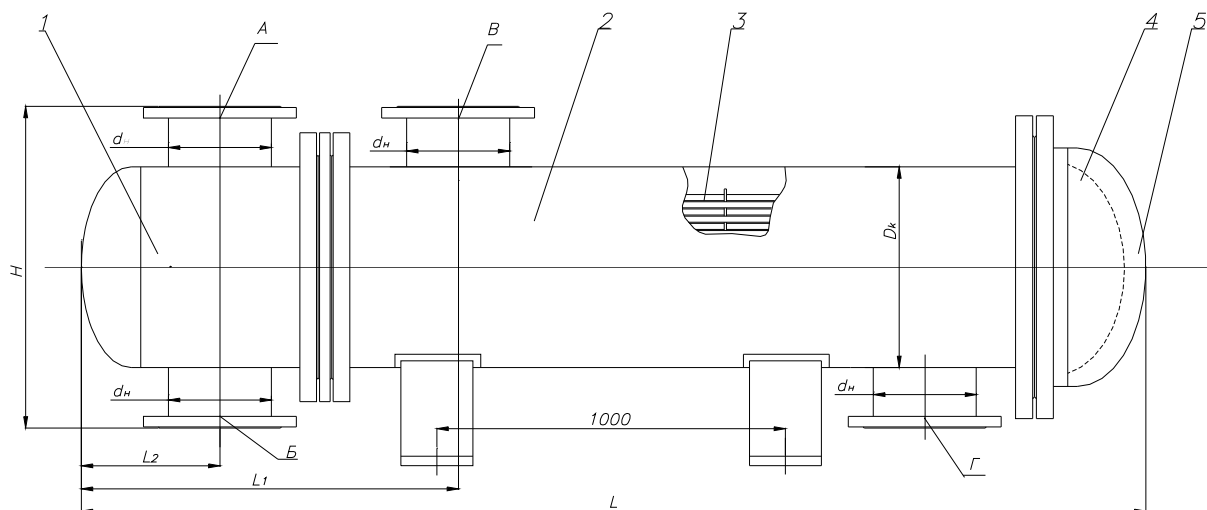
Схема подогревателя ПВМР: 1 – камера распределительная; 2 – корпус; 3 - трубная система; 4 – малая водяная камера; 5 – съемная часть корпуса; А – отвод сетевой воды; Б – подвод сетевой воды; В – подвод греющей воды; Г – отвод греющей воды.
